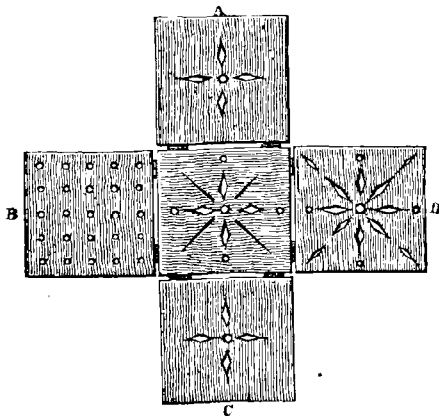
Assemblage des cinq faces à charnières de la machine Pellegrin.
